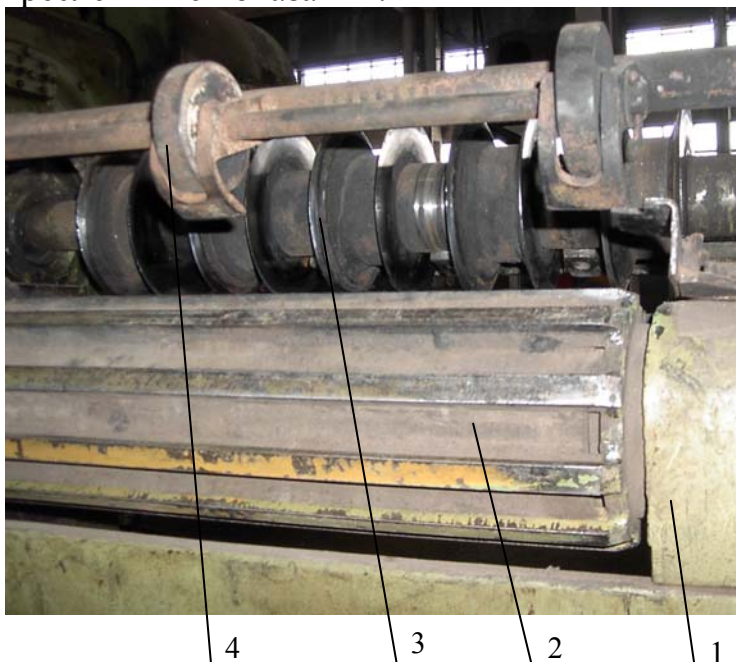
Конструкція зубчато-шліцевої передачі для подачі конвеєрної стрічки в зону різання:
